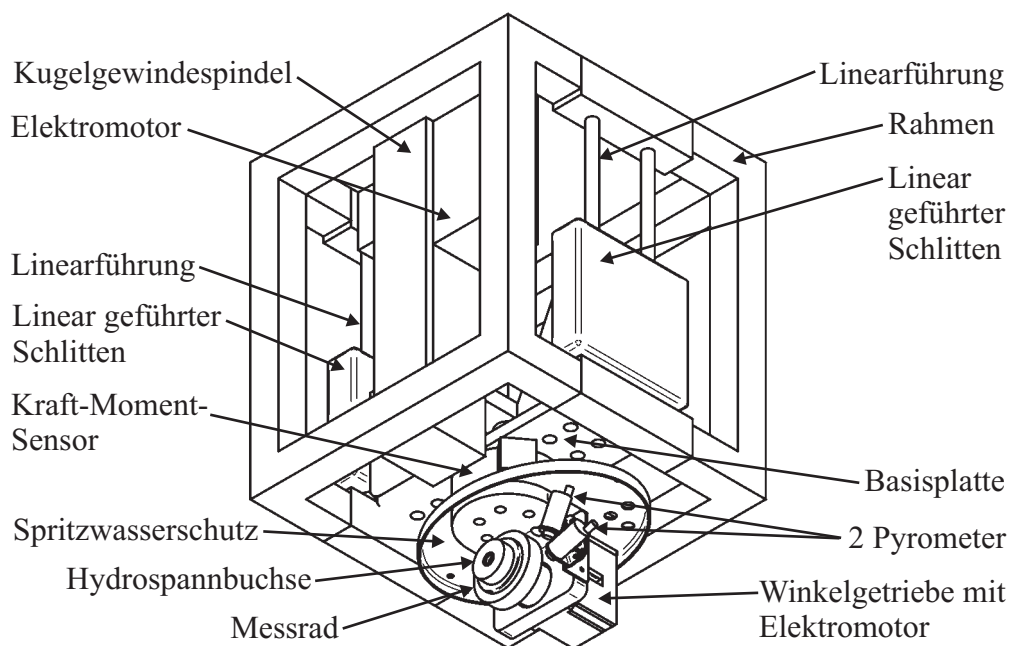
Skizze der Messeinrichtung des Messroboters
